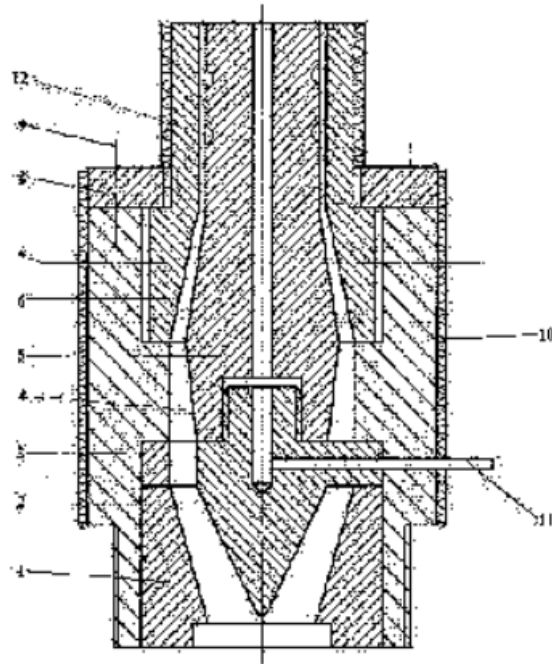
Головка екструдера з пластиковою жорсткою трубкою з ромбічним сердечником буфера [6]: 1 - блок; 2 – роздільник потоку; 3 - корпус форми; 4 - канал розплаву; 5 - оправка; 6 - матриця; 7 - регулювальний гвинт; 8 - сальник; 9 - кріпильний гвинт; 10 - нагрівальне кільце 11 - повітрозабірна штанга; 12 - буферна ємність
